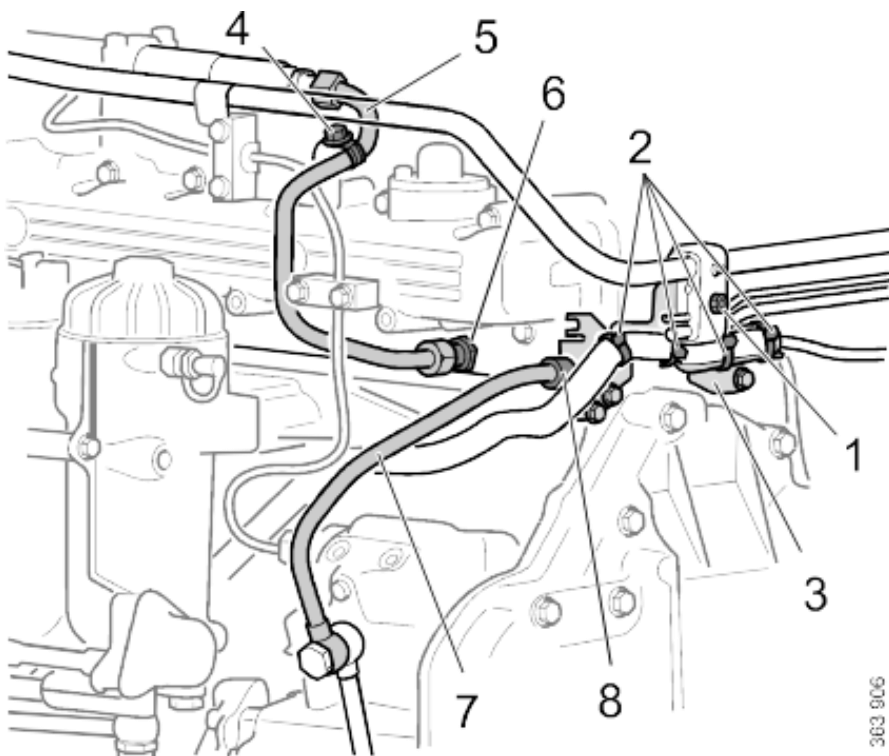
28 montaje tubos de combustible de la rampa. fuente: multiweb taller Scania Concepción.
